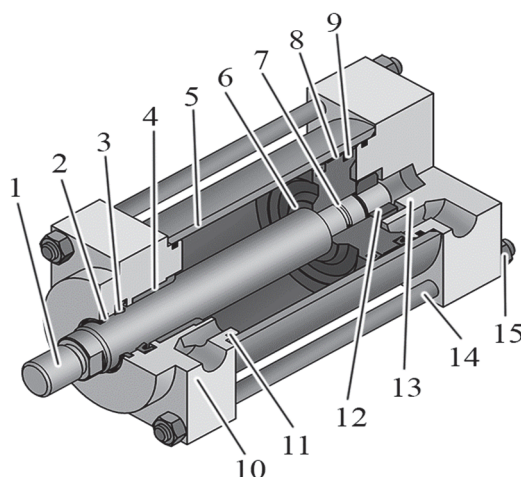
Конструкция пневмоцилиндра: 1 – шток; 2 – грязеуловительное кольцо; 3 – манжета штоковая; 4 – направляющая втулка; 5 – гильза; 6 – поршень; 7 – резиновое кольцо; 8 – поршневое кольцо; 9 – манжеты поршневые; 10 – передняя крышка пневмоцилиндра; 11 – резиновые кольца; 12 – гайка; 13 – задняя крышка; 14 – шпилька; 15 – гайка
